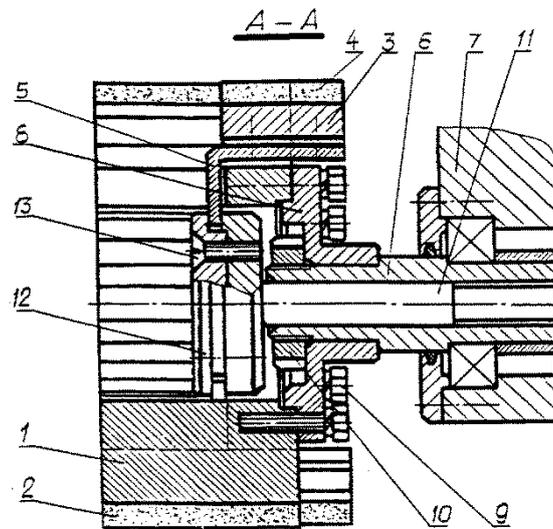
Круг для абразивной обработки заготовок [7]
